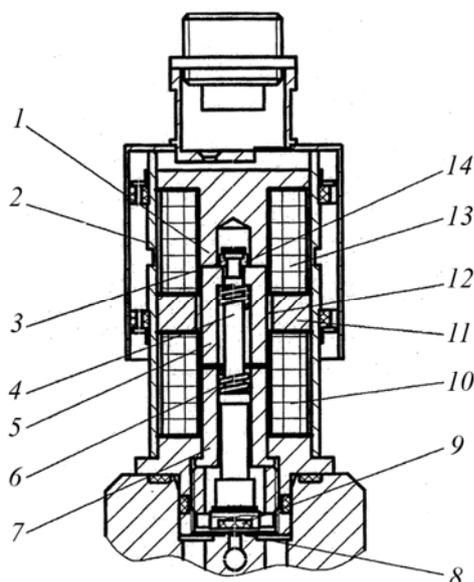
Конструктивная схема ЭМК с приводом типа ДТВ: 1 – верхний стоп; 2 – корпус клапана; 3 – шейка штока; 4 – шток; 5 – ползун (якорь); 6 – пружина; 7 – нижний стоп; 8 – седло; 9 – золотник с резиновой вставкой; 10 – нижняя обмотка; 11 – постоянный магнит; 12 – трубка разделительная; 13 – верхняя обмотка; 14 – шайба стопорная
